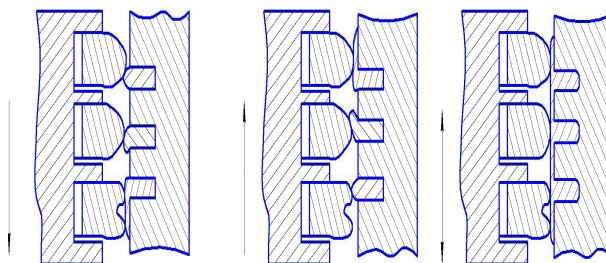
Схема образования плёнки на поверхности гильзы цилиндров: 1-поршень; 2-поршневое кольцо; 3-гильза цилиндра; 4-вставка
